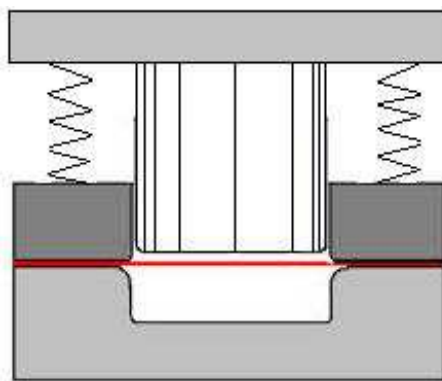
Outil d'Emboutissage à Serre-Flan, placé sur une Presse à Simple Effet
